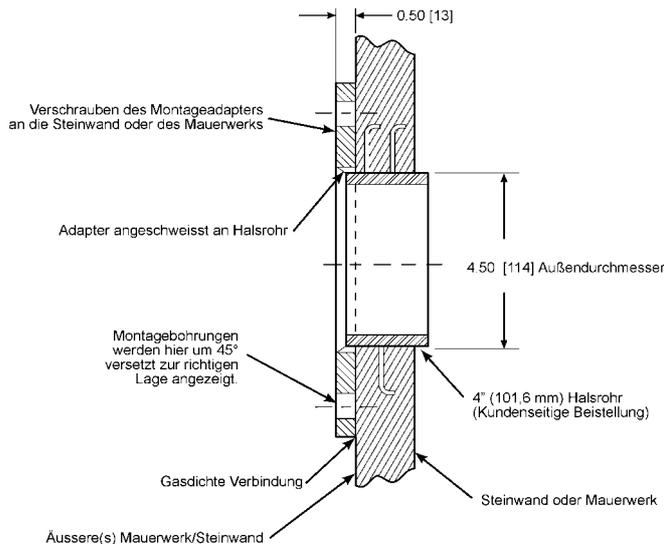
Abmessungen der Montageadapter für Oxymitter 4000
